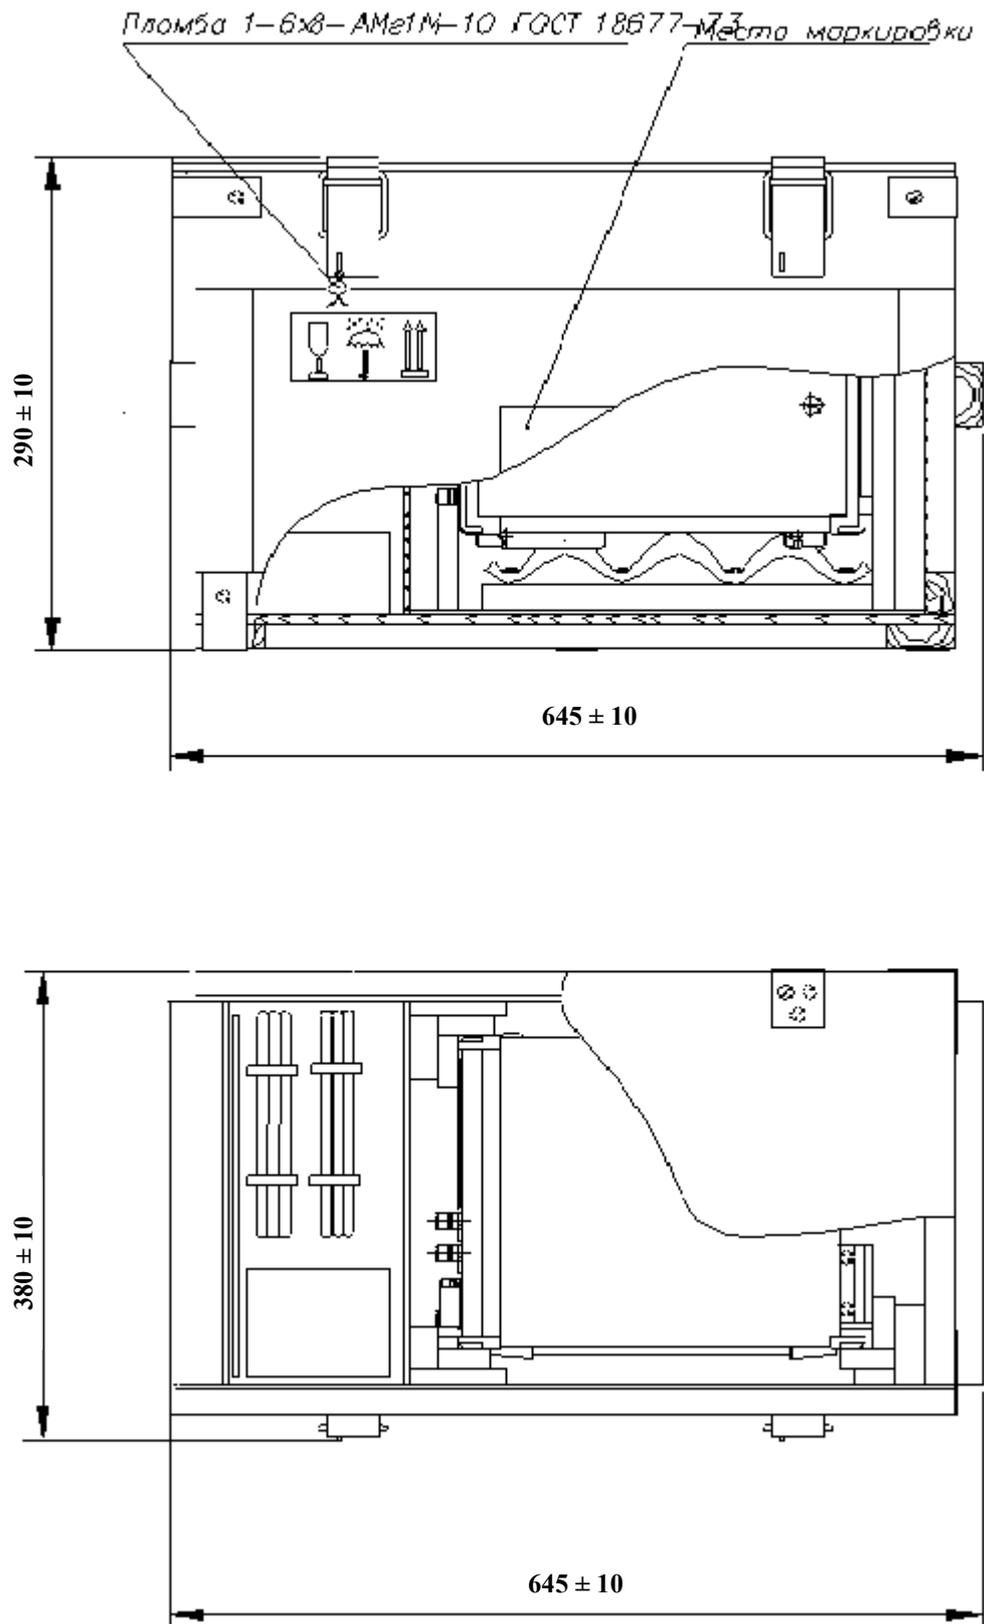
Габаритные размеры укладочно-транспортной тары
